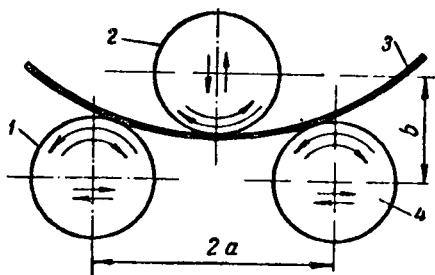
Схема получения гибкой детали цилиндрической формы на копировально-гибочном станке по симметричной схеме
